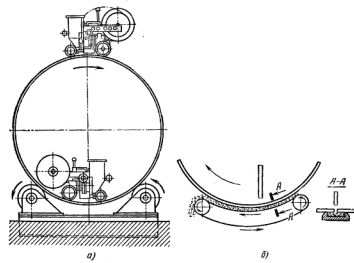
Стенд для зварювання кільцевих швів (а); флюсова підшукка (б)
